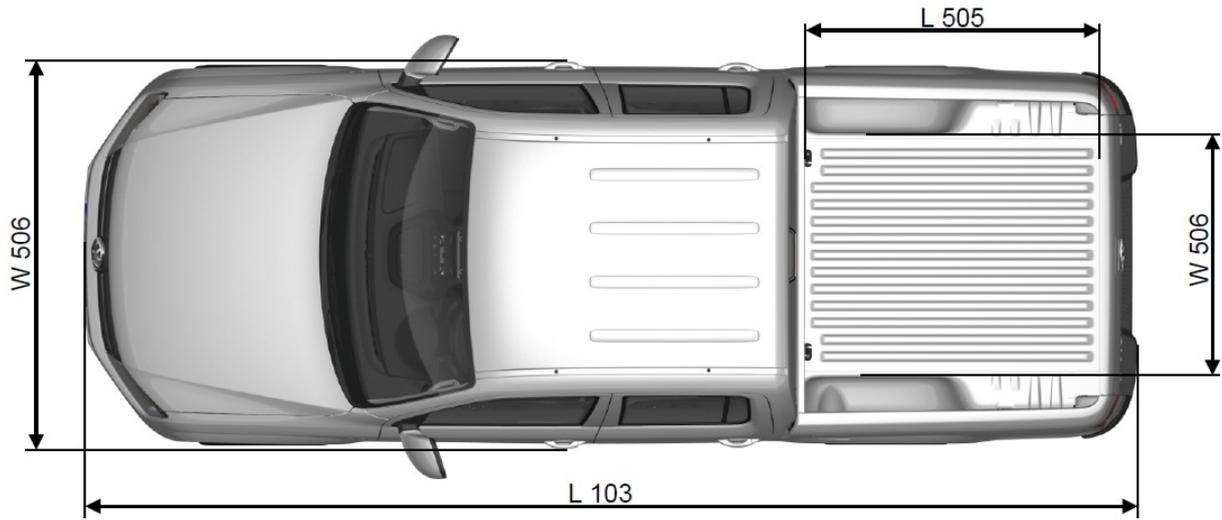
Draufsicht AMAROK-DC (Double Cab)
